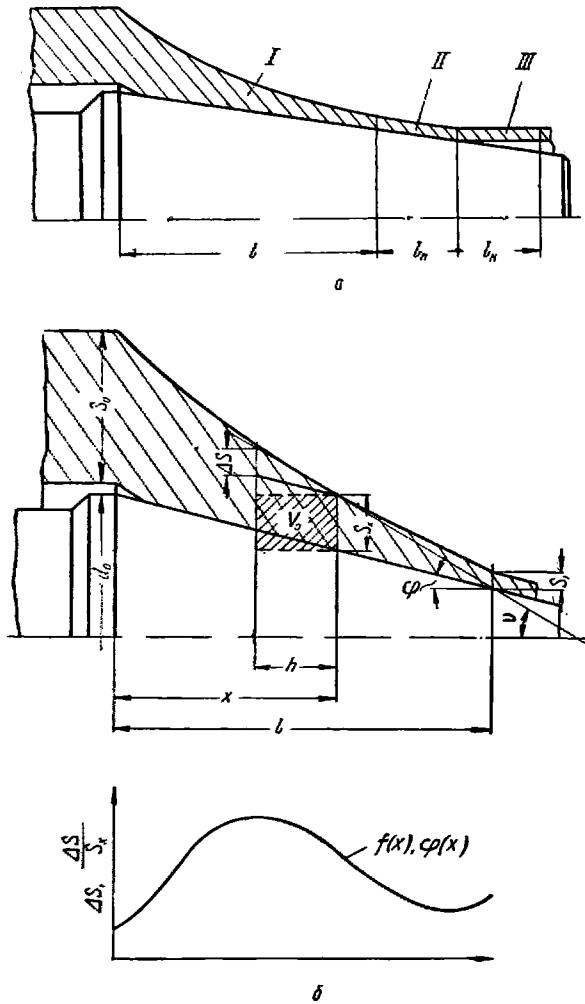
Схема к расчету калибровки валков стана холодной прокатки труб
